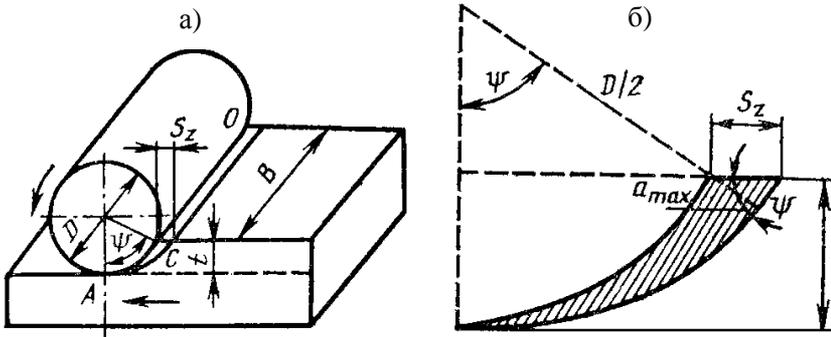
Схема и элементы режима резания при фрезеровании
